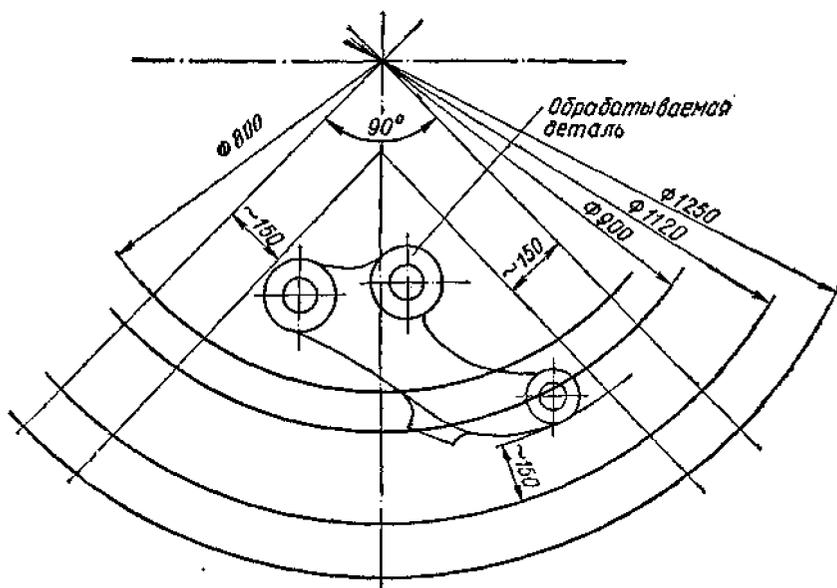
Схема для определения диаметра планшайбы поворотного стола агрегатного станка
